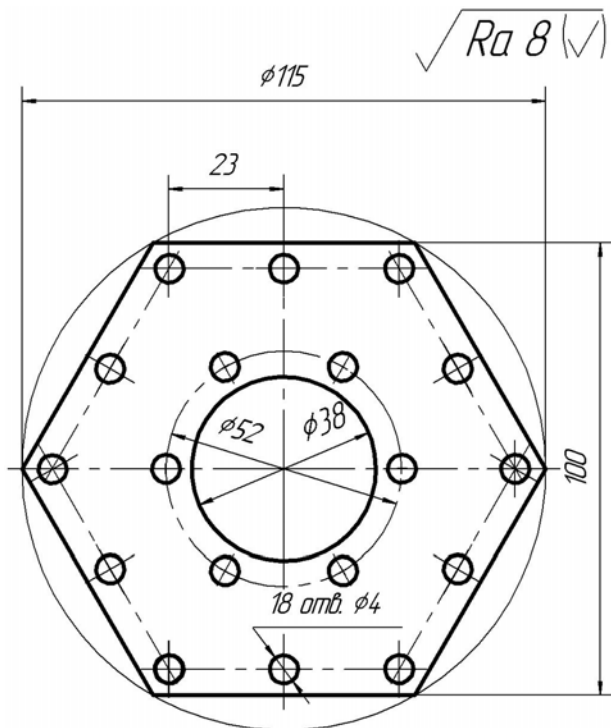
Кресленик деталі фрезерного напівавтомата
